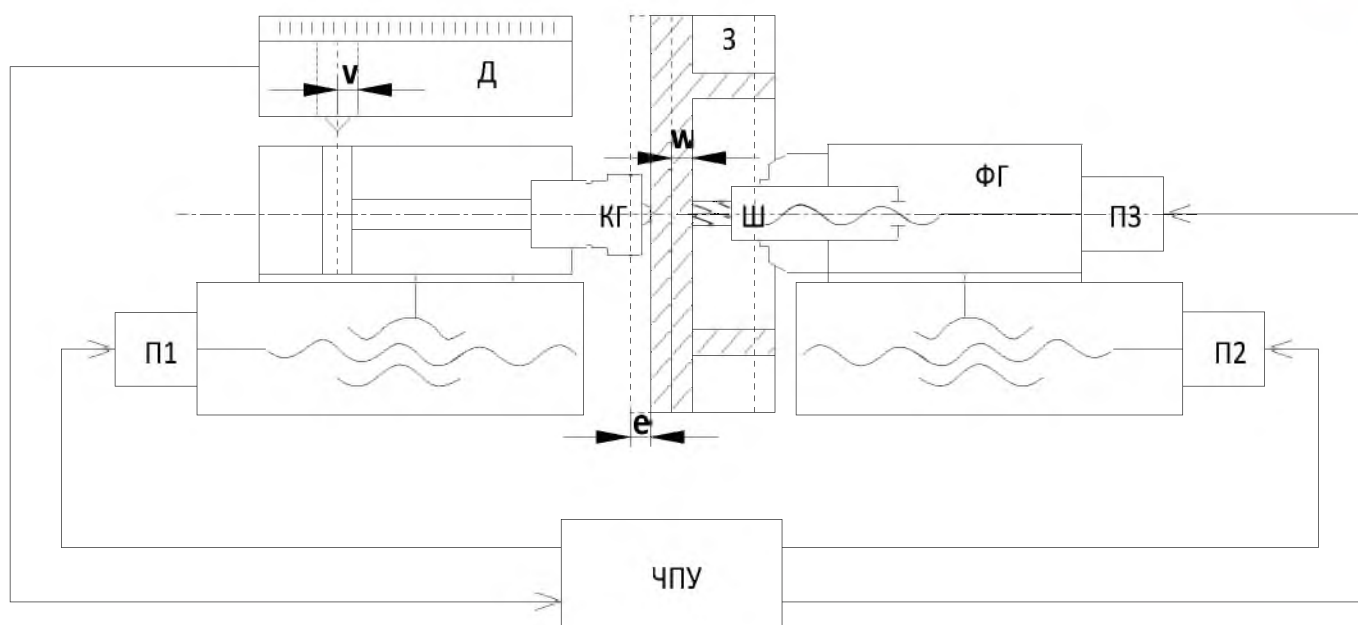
Схема станка с ЧПУ для осуществления зеркального фрезерования:
